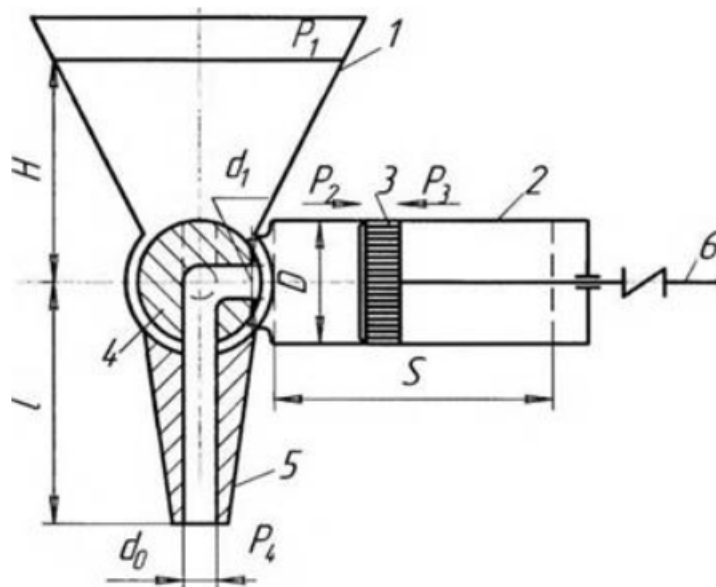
Дозувальний пристрій поршневого типу: 1 — ресивер; 2 — циліндр для дозування; 3 — поршень; 4 — шаровий кран; 5 — насадка; 6 — привідний важіль.
